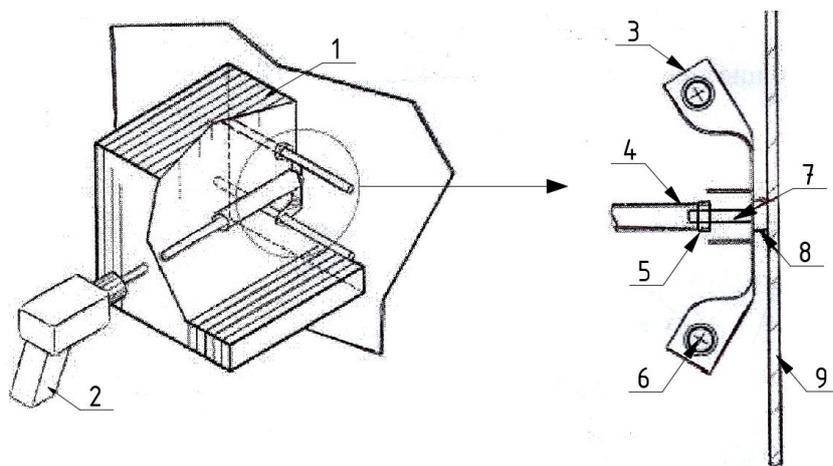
Схема крепления керамоблока контактной сваркой
